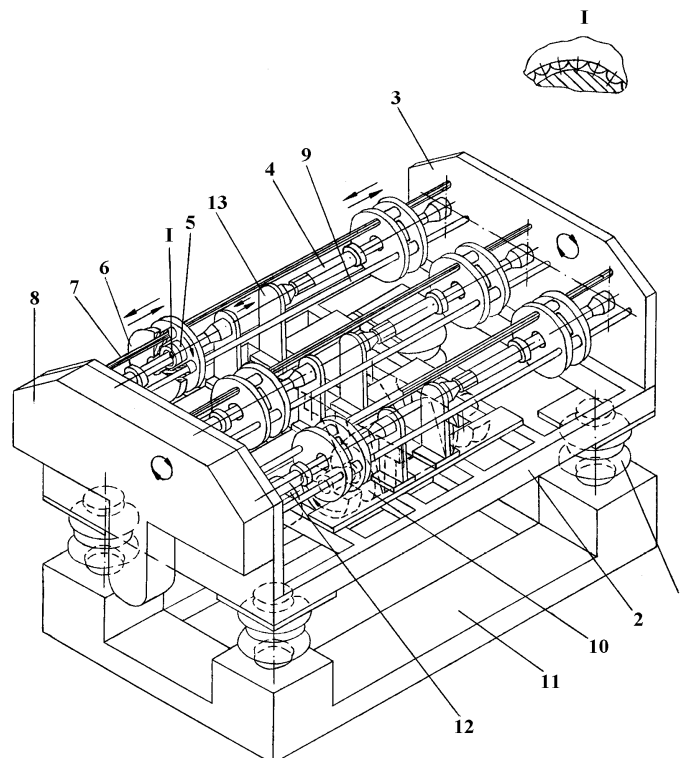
Принципова схема вібраційно-відцентрової зміцнювальної установки
